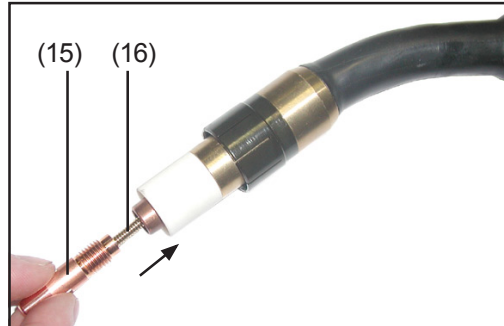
Repousser l'âme guide-fil et visser le tube-contact
